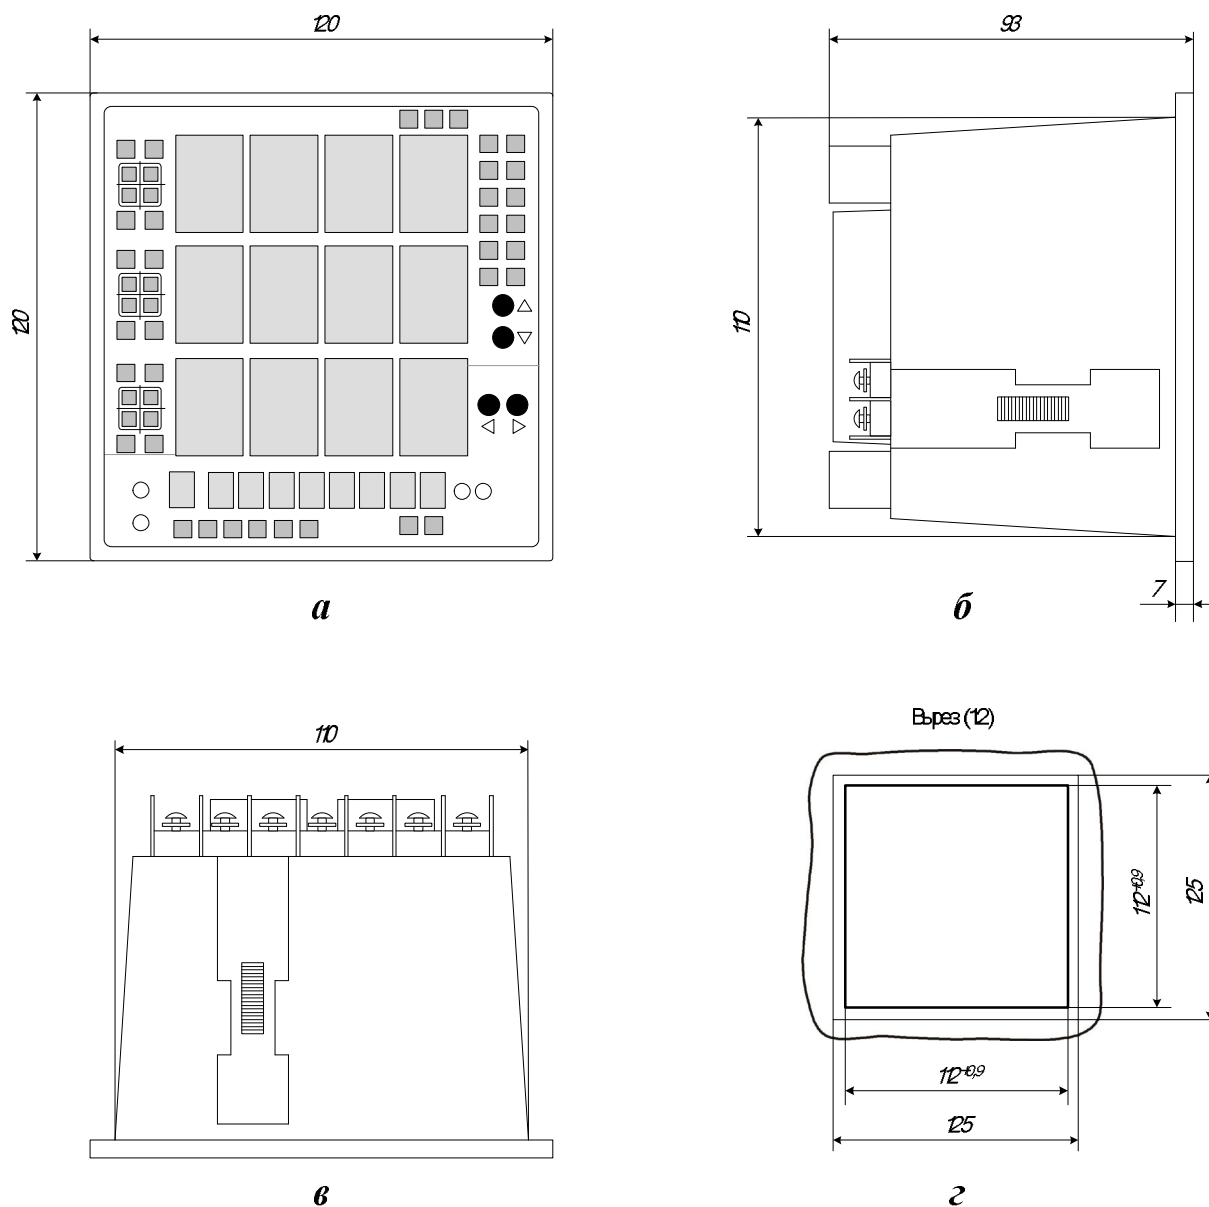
Общий вид, габаритные и установочные размеры прибора ЦМК120С:
